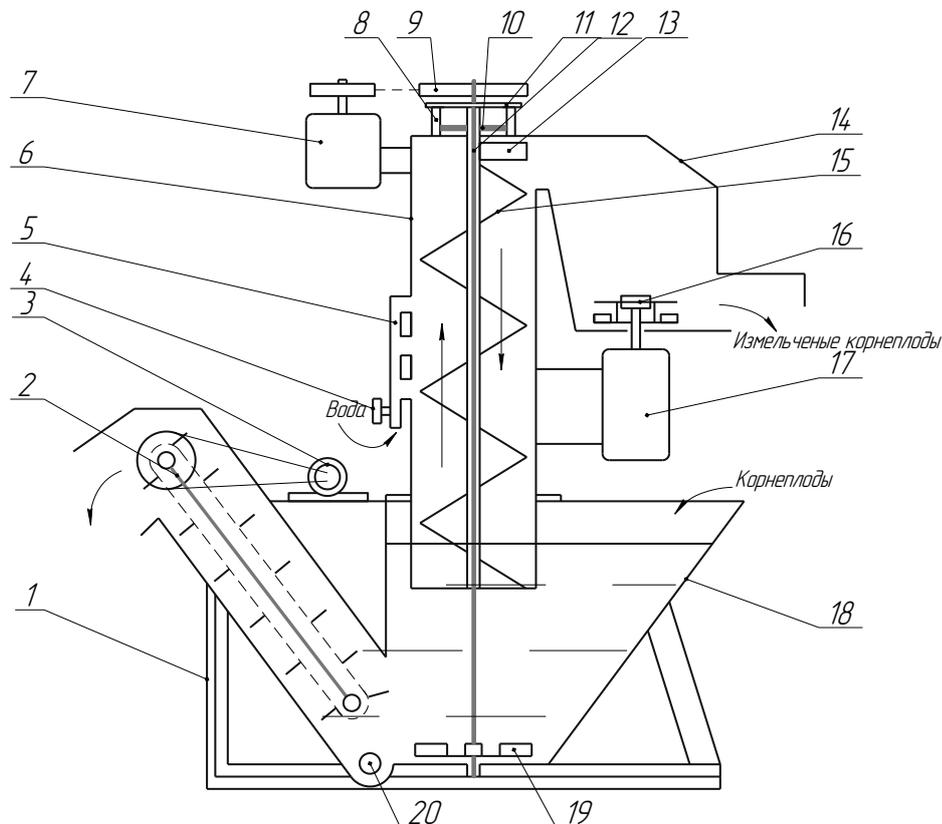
Схема вибрационно-шнековой мойки ВШМ-5: 1 - рама; 2 - транспортер-камнеуловитель; 3, 7, 17 - электродвигатели; 4 - вентиль; 5 - коллектор для подвода воды; 6 - кожух шнека мойки; 8 - ролик; 9 - шкив; 10 - соединительная ось; 11 - диск; 12 - вал; 13 - выбрасыватель; 14 - крышка измельчителя; 15 - шнек; 16 - измельчитель; 18 - моечная ванна; 19 - крылач; 20 - люк
